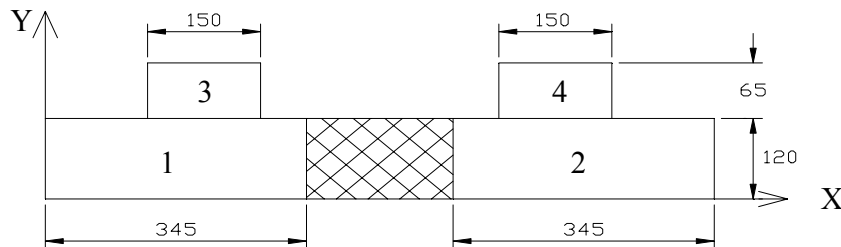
Forma geométrica y principales dimensiones del cubo.
